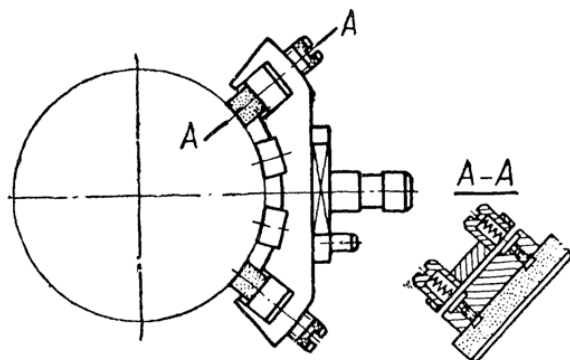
Головка для суперфиниширования шеек коленчатого вала
